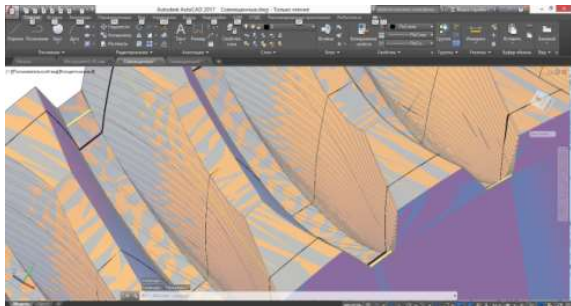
Рабочая поверхность цилиндрического червячного колеса
